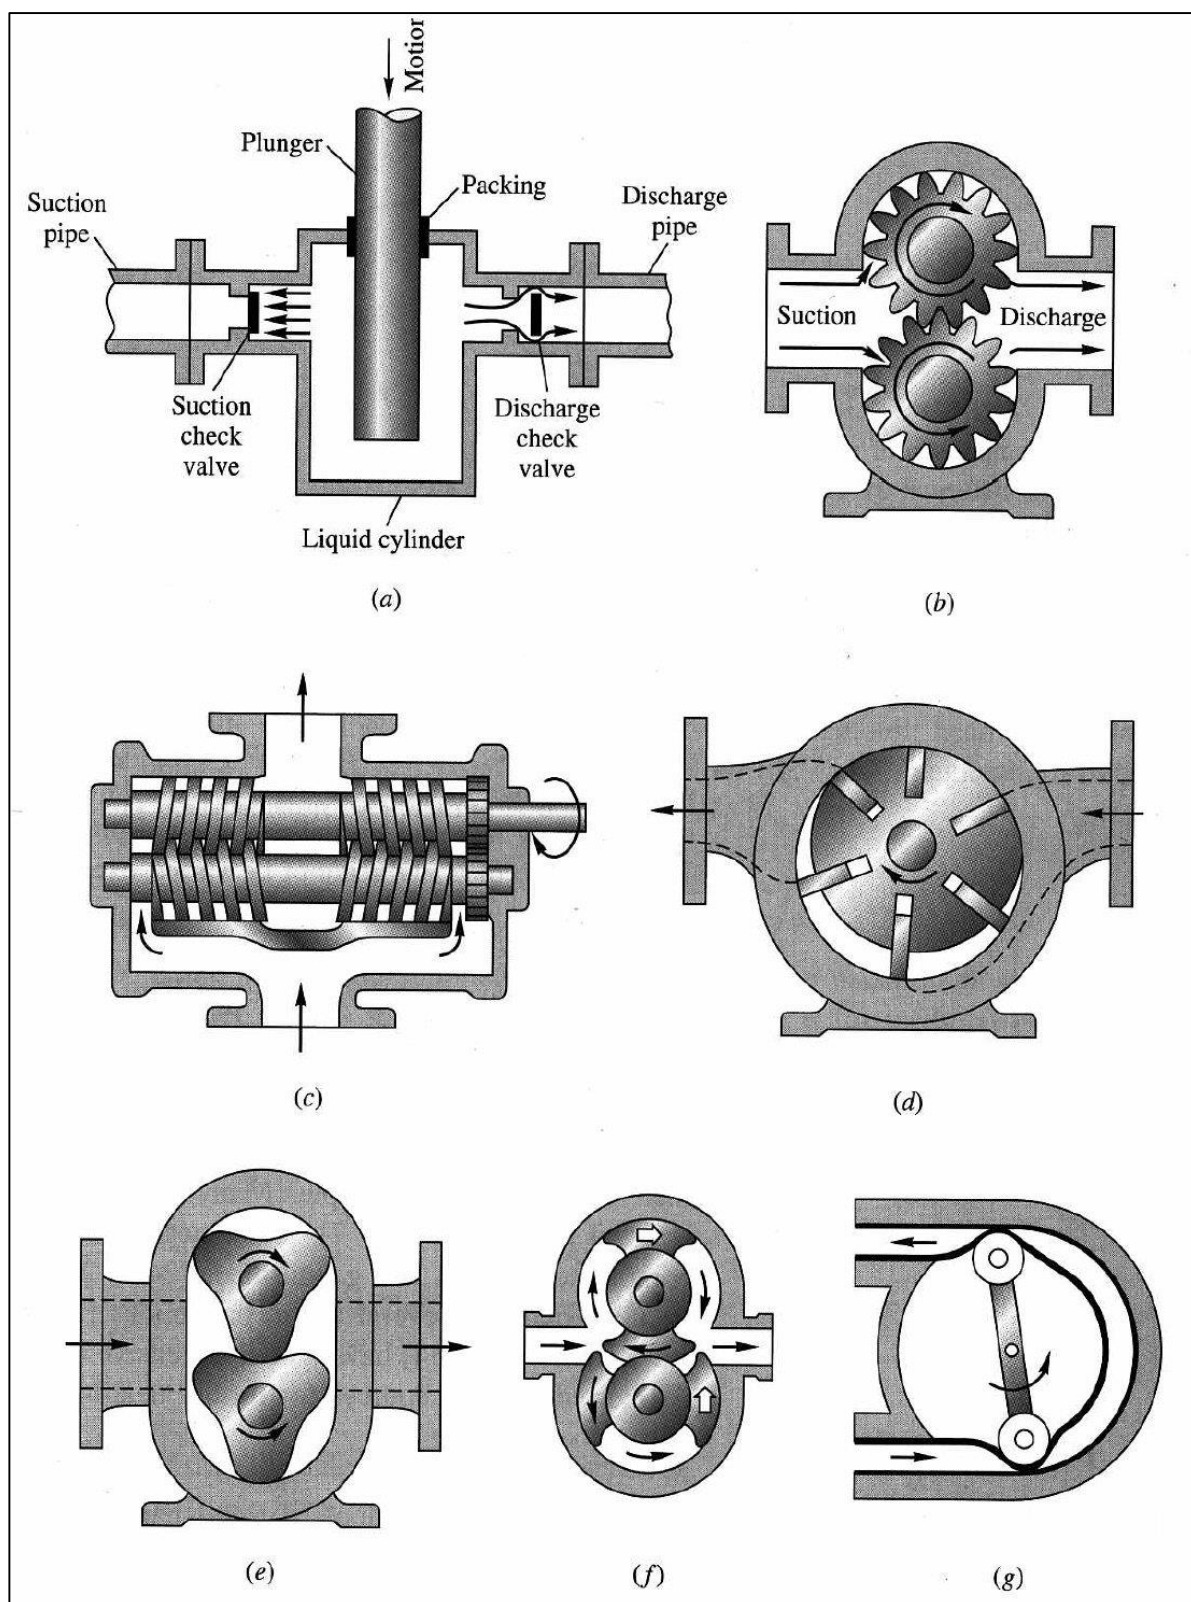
Exemplos de bombas de deslocamento positivo. (a) Bomba de êmbolo; (b) Bomba de engrenagens; (c) Bomba helicoidal; (d) Bomba de palhetas; (e) Bomba de lóbulos triplos; (f) Bomba de pistão duplo circunferencial; (g) Bomba de tubo flexível ou de rolete. (Fonte: BRASIL, 2013)
